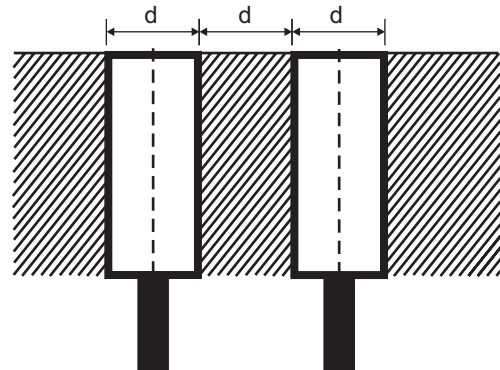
Lange Ausführung, Nicht bündiger Einbau, Steckversion
